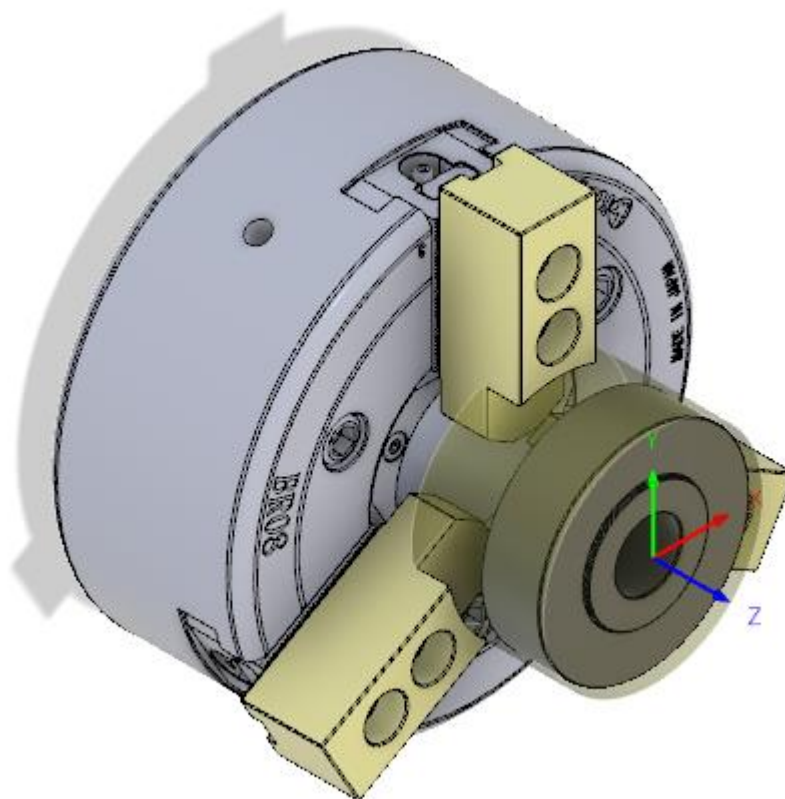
Створення установу та розміщення деталі та заготовки
